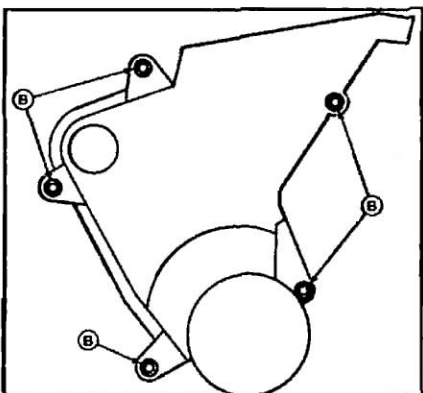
Расположение болтов крепления нижнего кожуха зубчатого ремня
